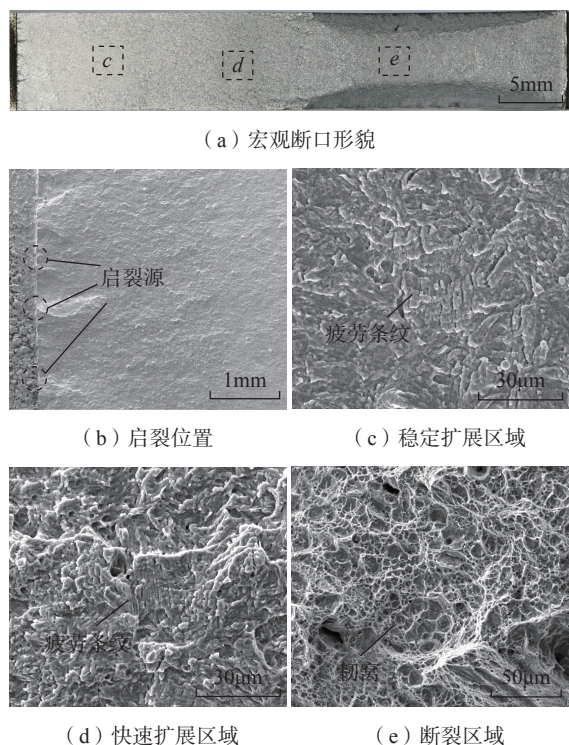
30CrMnSiNi2A 超高强度钢电子束焊接头热影响区疲劳裂纹扩展速率试样的断口形貌
